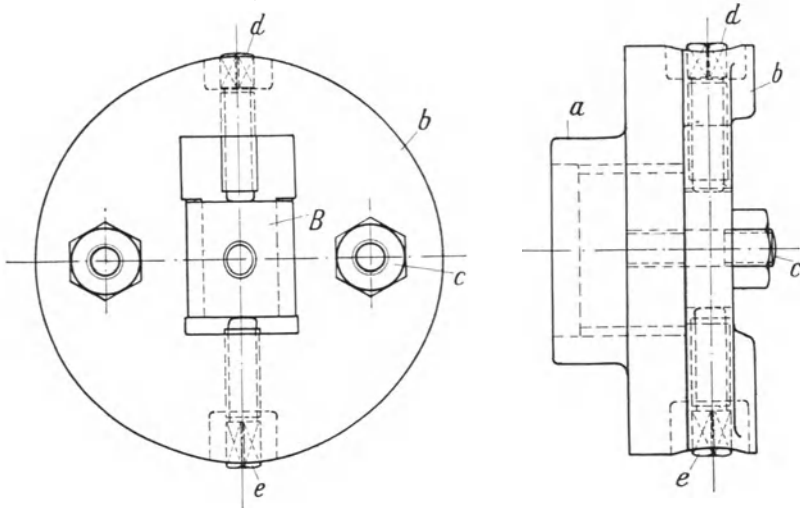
Bohren und Gewindeschneiden in den Backen zu Abb. 529.
